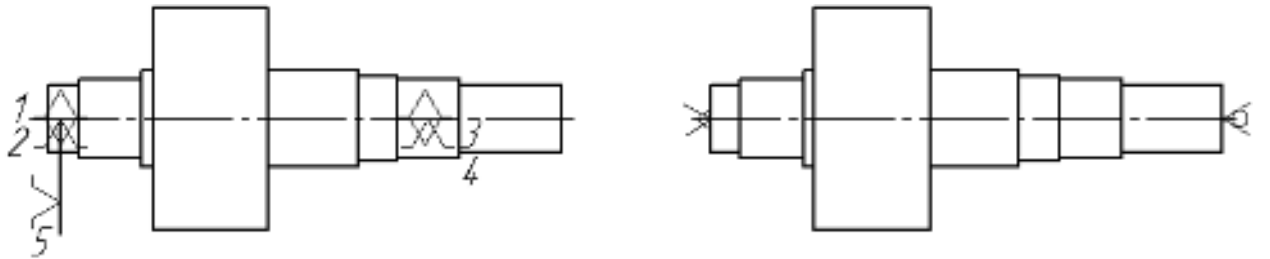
Схема базування і закріплення деталі на токарних операціях
